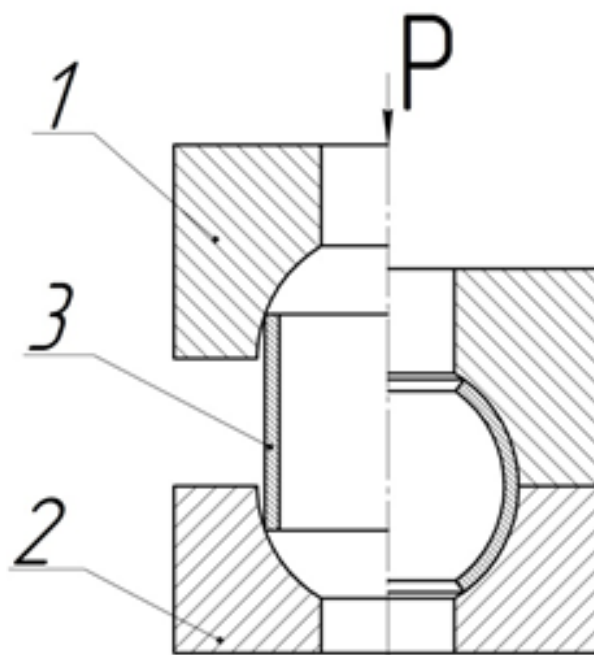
Схема обжима трубной заготовки: 1 – верхняя полуматрица, 2 – нижняя полуматрица, 3 – заготовка
